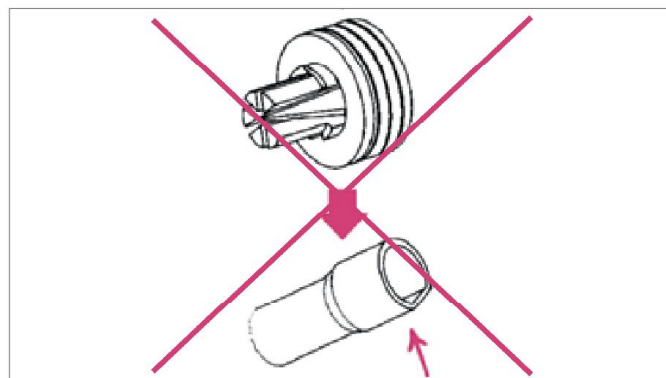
Повреждение трубы из-за дефектной расширительной насадки
